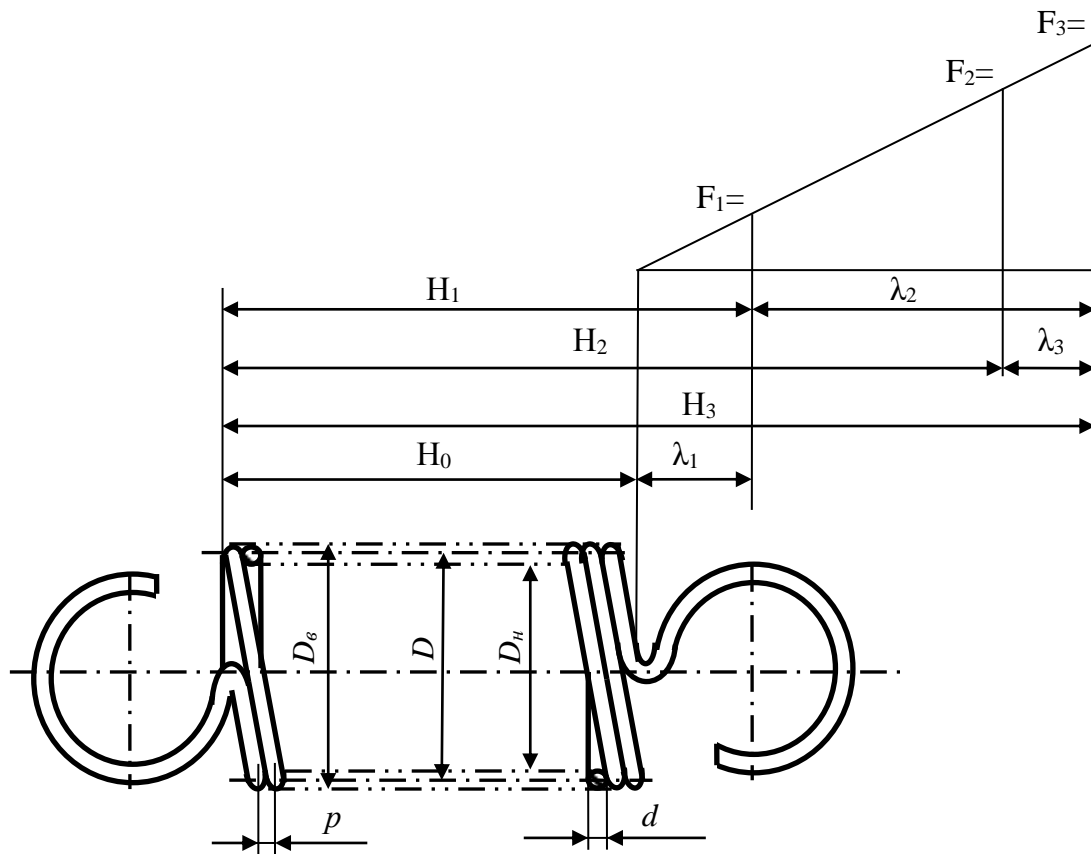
Оформление чертежа детали «Пружина растяжения»
